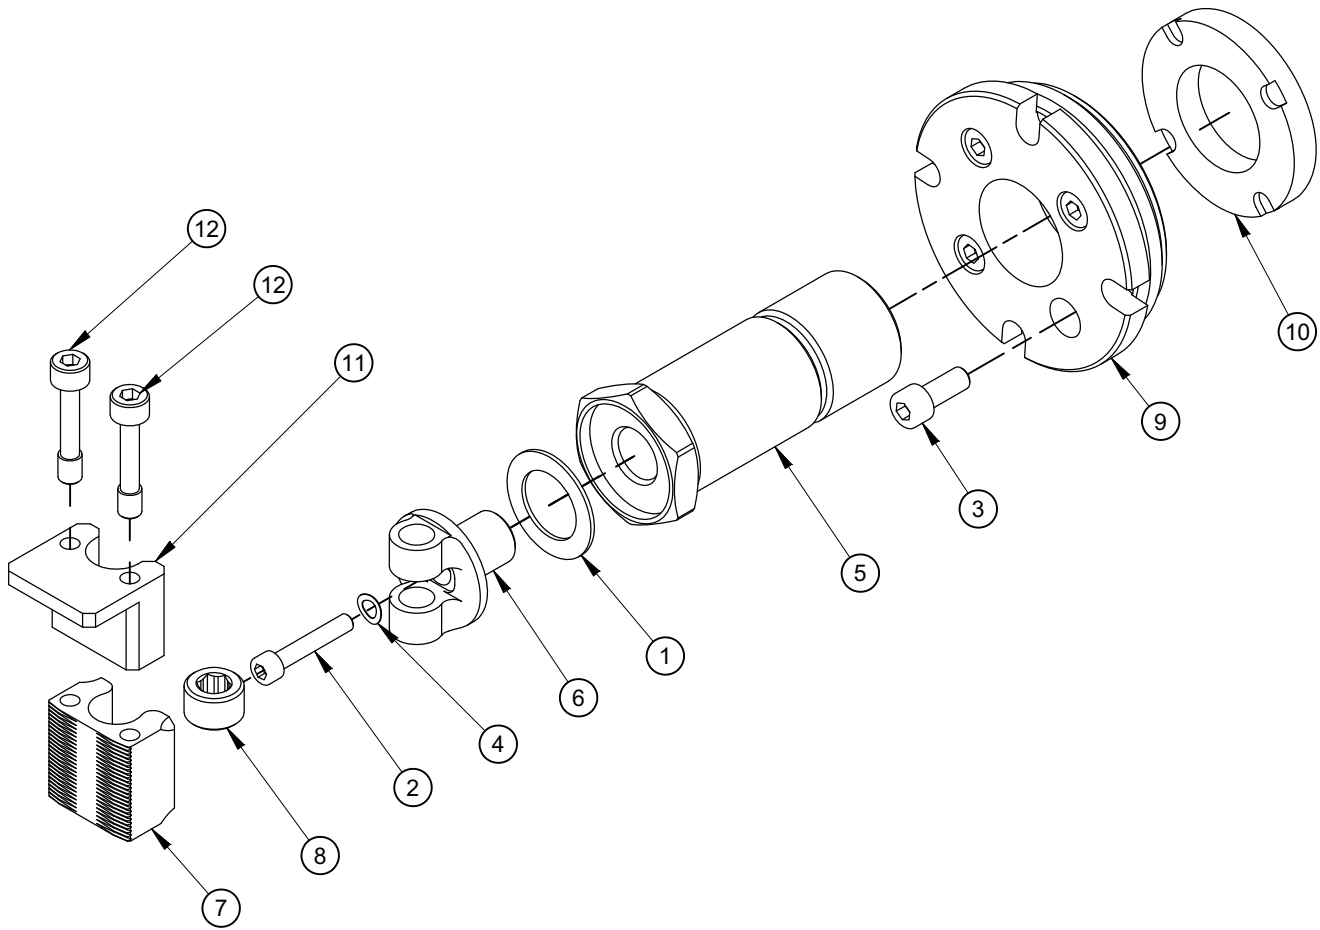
P/N 87916 ENSEMBLE SOUPEPE D'AIR
